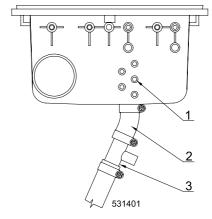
B Trémie à lessives liquides - Vue arrière
